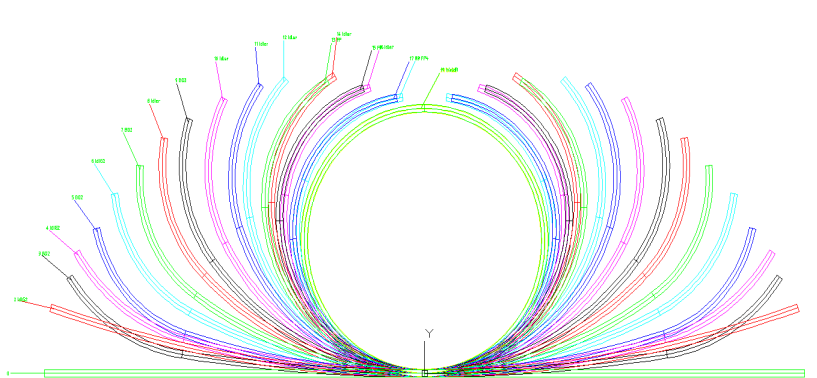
Маршрут формообразования трубной заготовки – «цветок»
